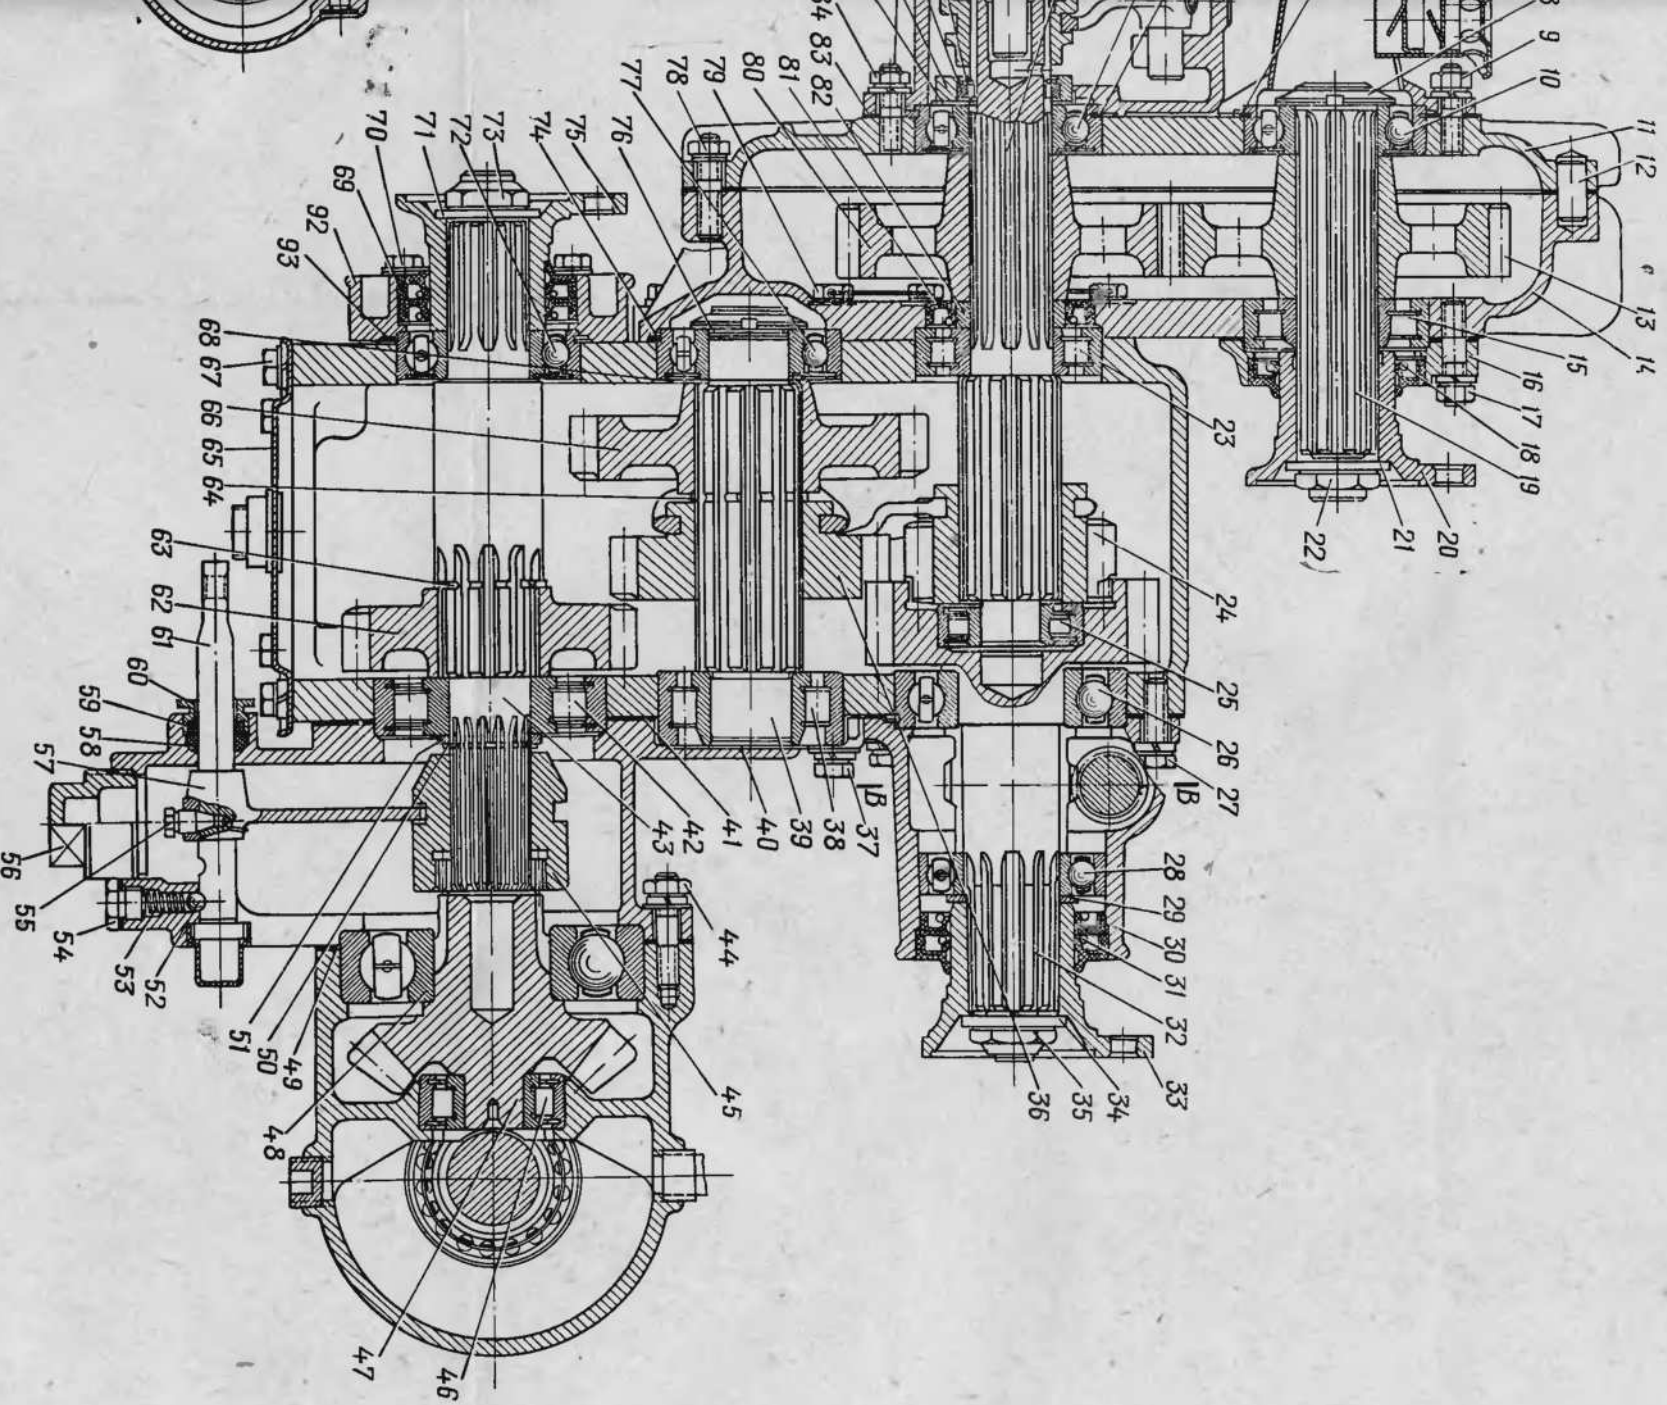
Раздаточная коробка с редуктором и коробками отбора мощности:
